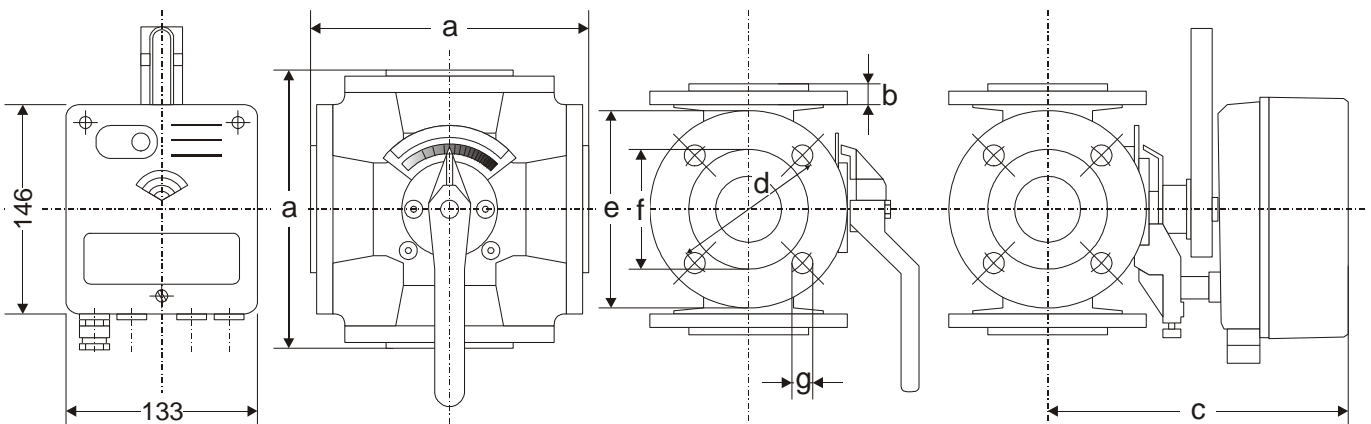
VMM et ZRxxxFA, dimensions (en mm)
